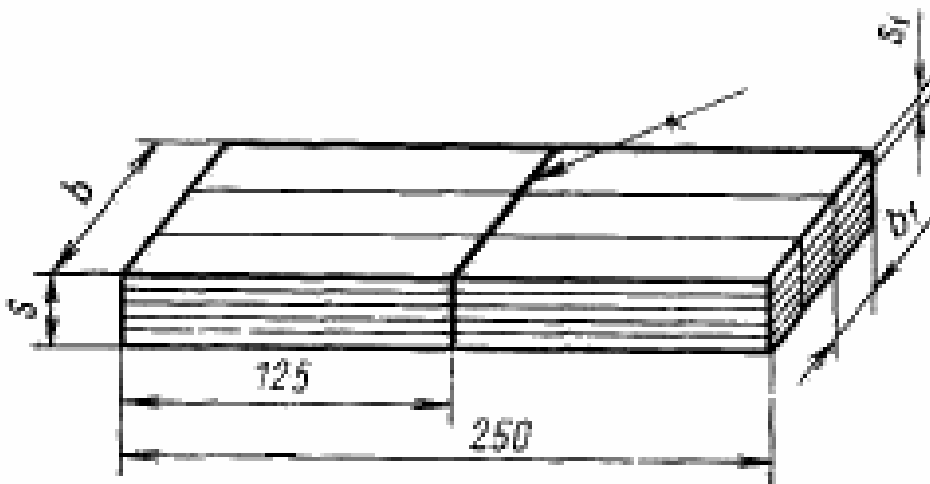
Заготовка та схема розкрою її на зразки
